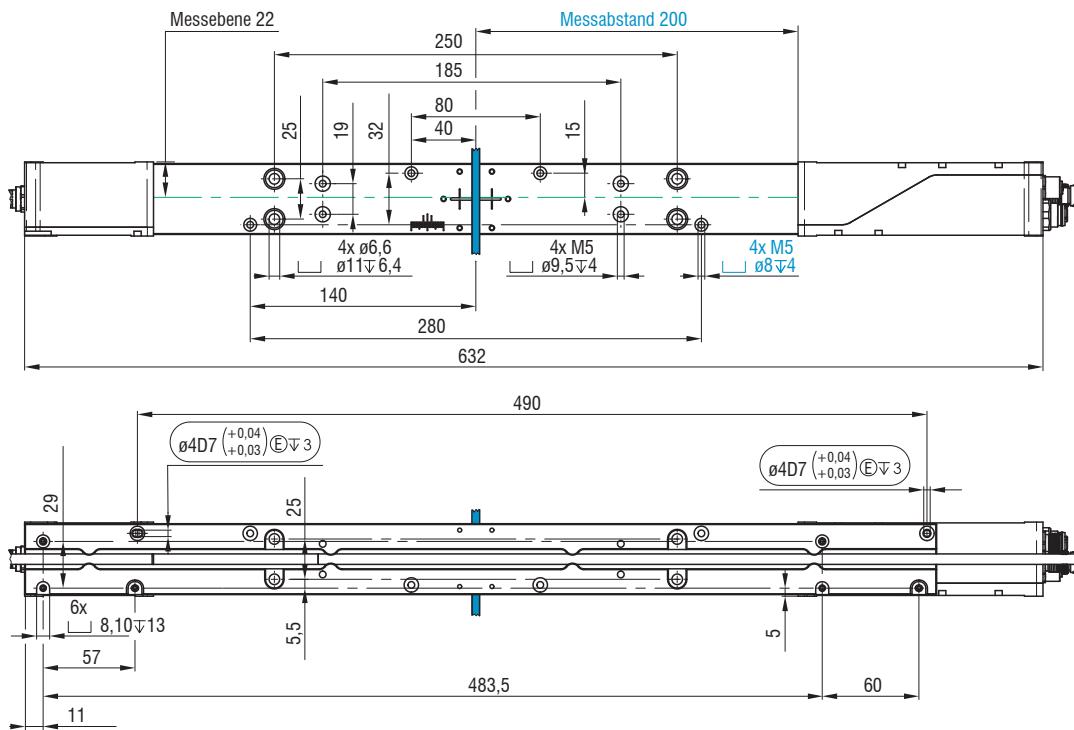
Maßzeichnung Lichtquelle und Empfänger ODC2700-40(002) mit Montageschiene, Abmessungen in mm
